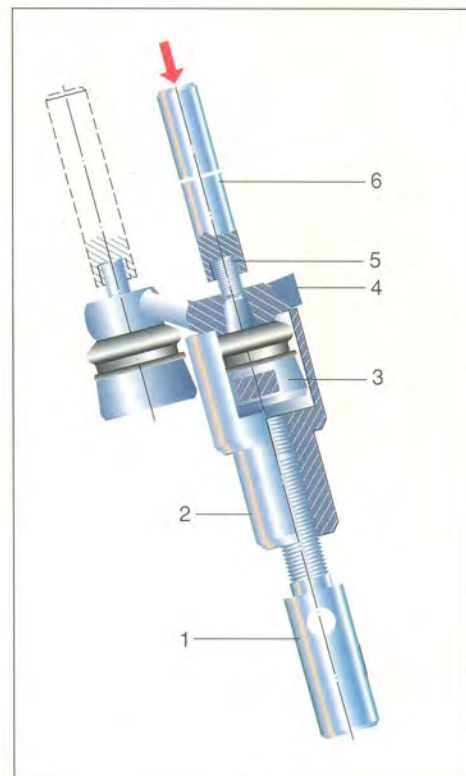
Приспособление для выпрессовки рулевого пальца из сошки (маятникового рычага): 1 – винт; 2 – упор; 3 – корпус шарнира; 4 – сошка (маятниковый рычаг); 5 – палец; 6 – стержень.
